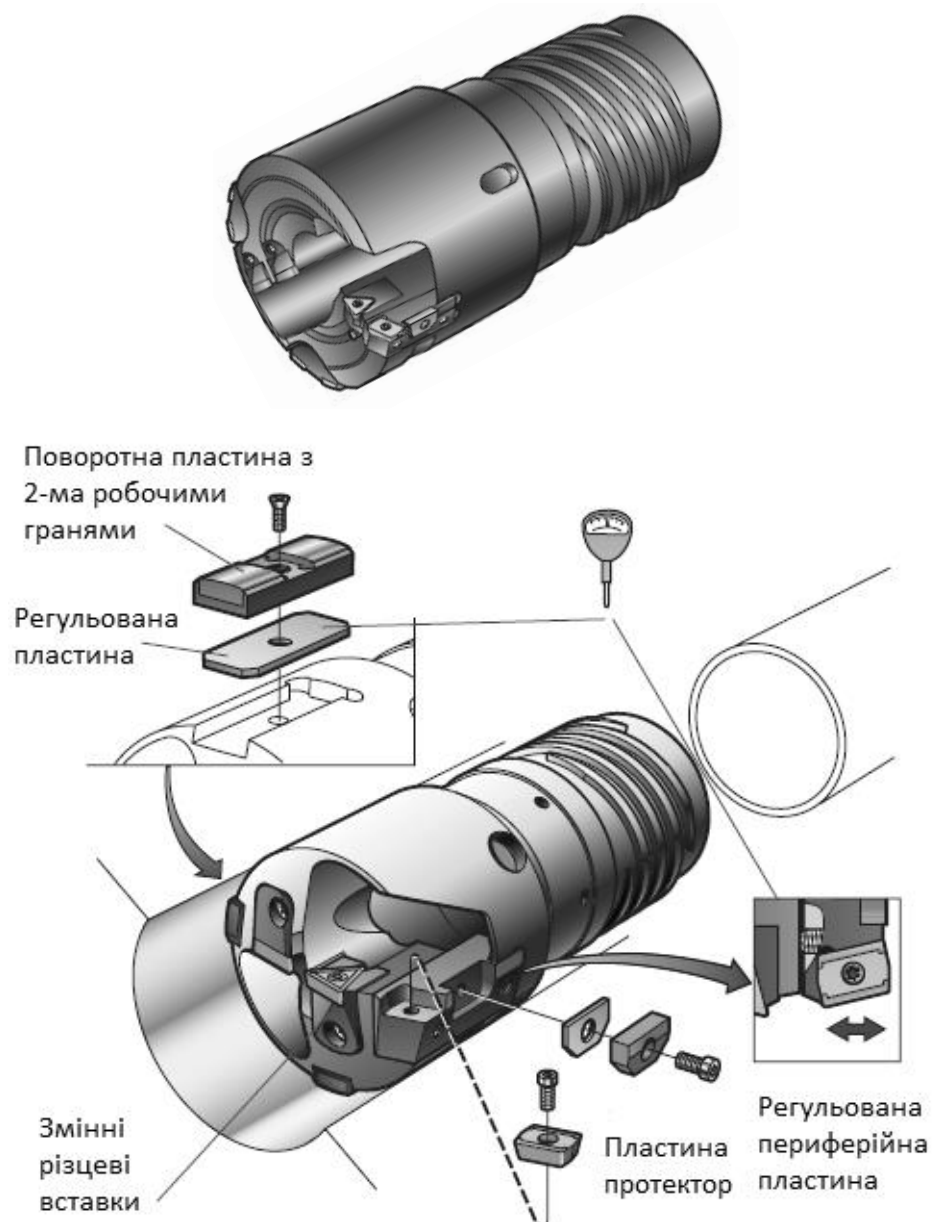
Загальний вигляд і конструктивна особливість свердлильної головки типу T-Max [8]
